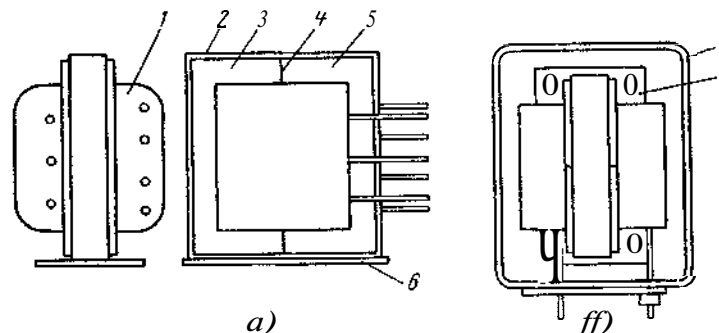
Конструкция высоковольтного трансформатора в изоляционном корпусе: а — до установки в корпусе, б — после установки в корпус перед заливкой компаундом
